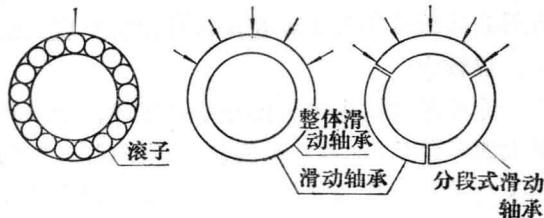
滚动轴承，整体滑动轴承和分段滑动轴承的受载情况比较。滑动轴承为面接触，滚动轴承为线接触
